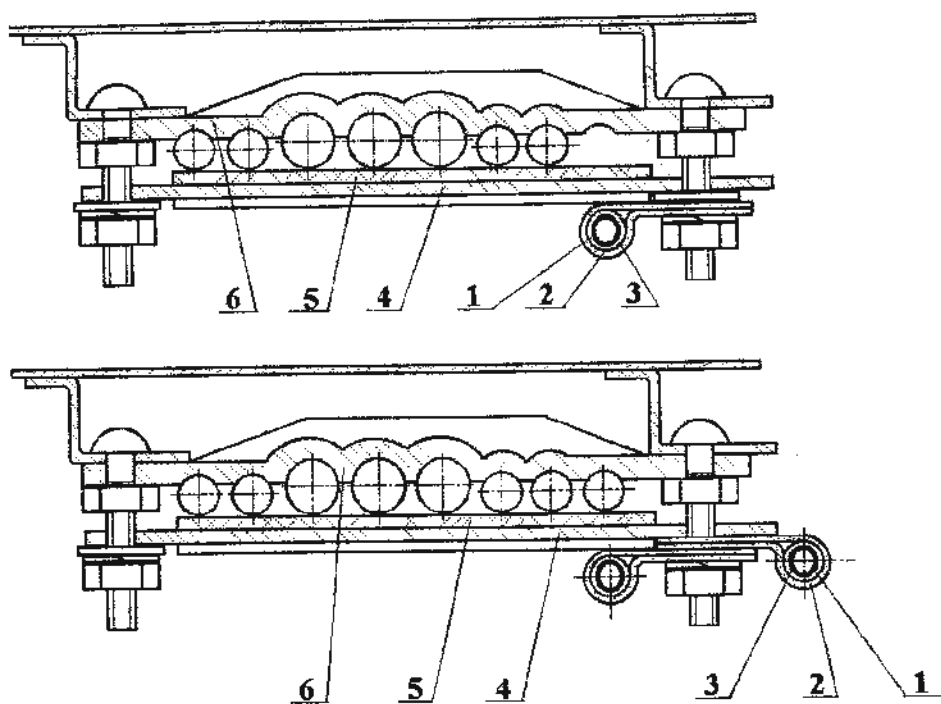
Крепление трубопровода на боковой стенке бункера:
